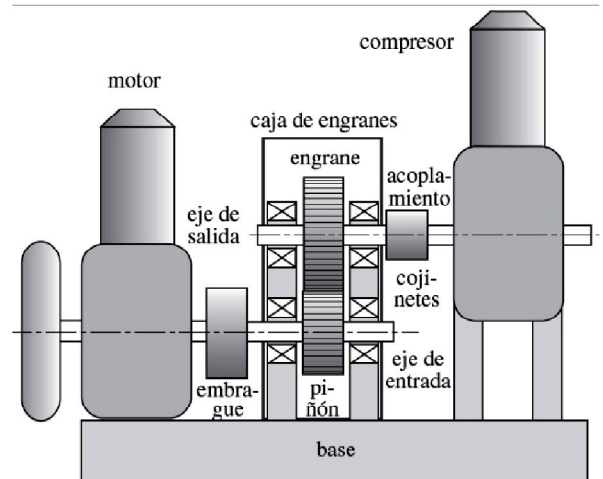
Mando de compresor, compuesto por un motor, volante de inercia, embrague, reductor de engranajes y acoplamiento. (Ref. 3)
